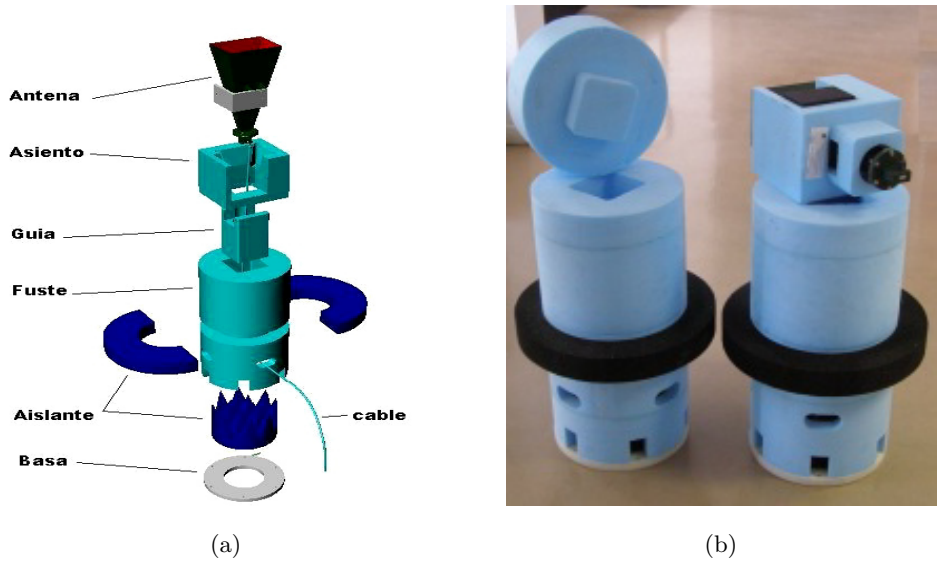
Columna de sujeción de blanco: (a) Diseño CAD (b) Imagen real
